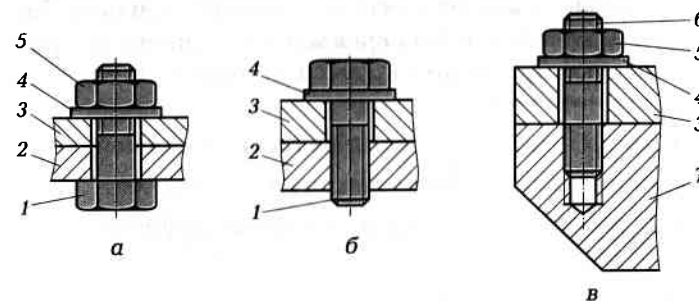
Конструктивные схемы резьбовых соединений:
